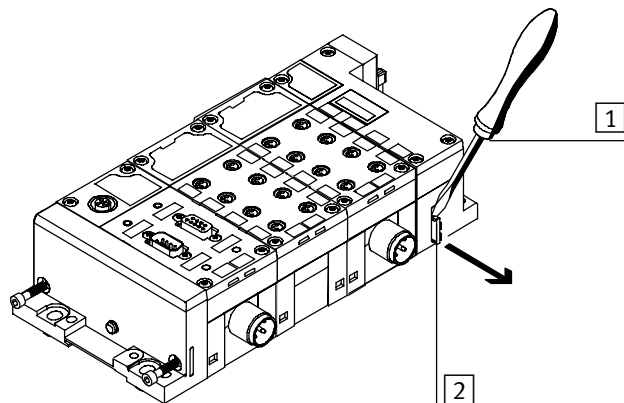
/5: Befestigungs- und Sicherungsblech im Pneumatik-Interface
